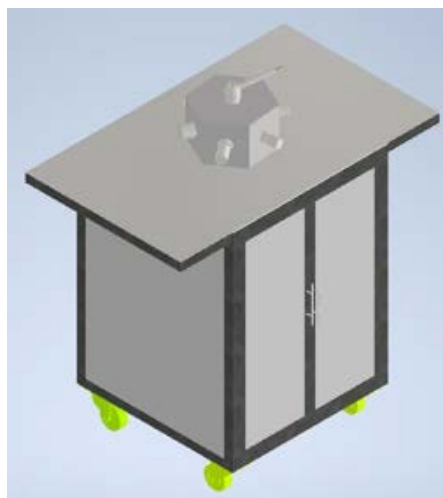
Ensamblaje final del módulo de montaje y desmontaje de rodamientos.
